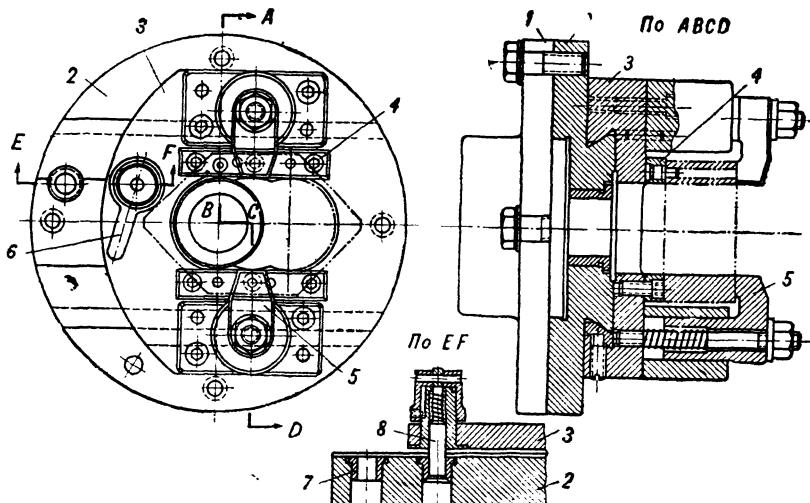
Передвижное приспособление для обработки корпуса масляного насоса.
